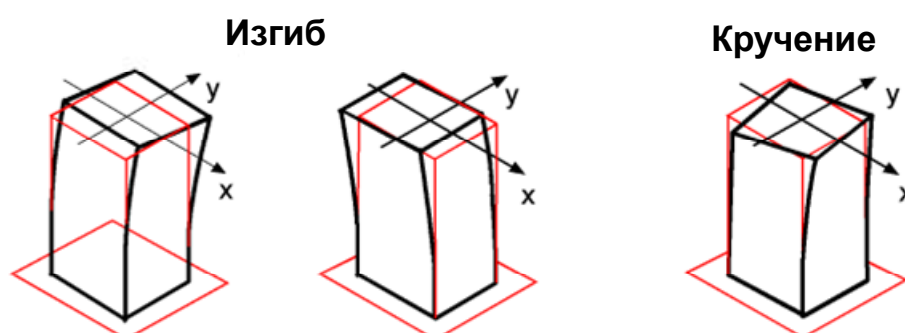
Типичные формы собственных колебаний корпусных деталей станков
